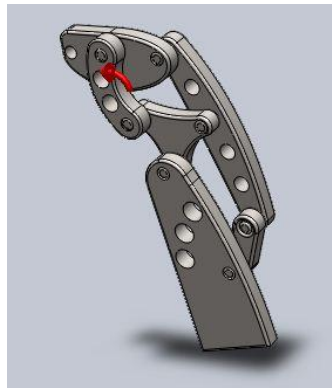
Mecanismo de seis barras, aplicado un motor de interpolador indicada con la flecha roja. Solidworks©
